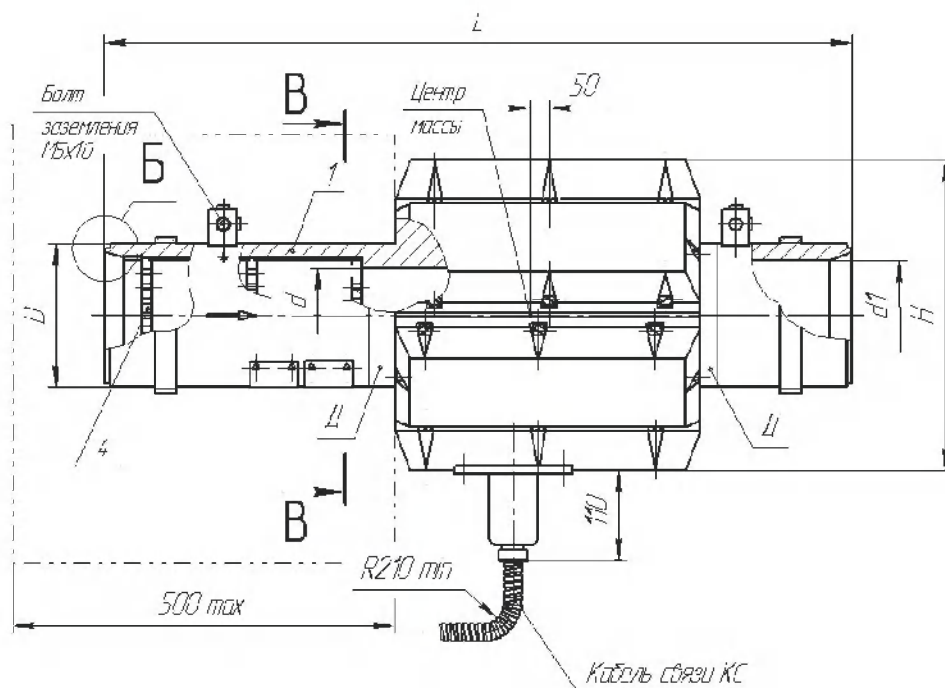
Первичный преобразователь ПП6-Р (соединение сварное)
